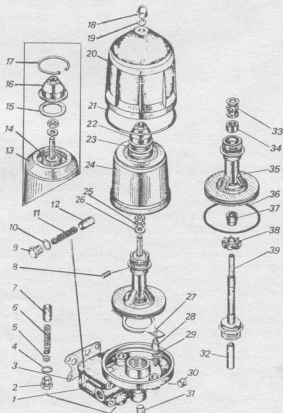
Фильтр центробежный масляный устанавливаемый на двигателях до № 28200:
